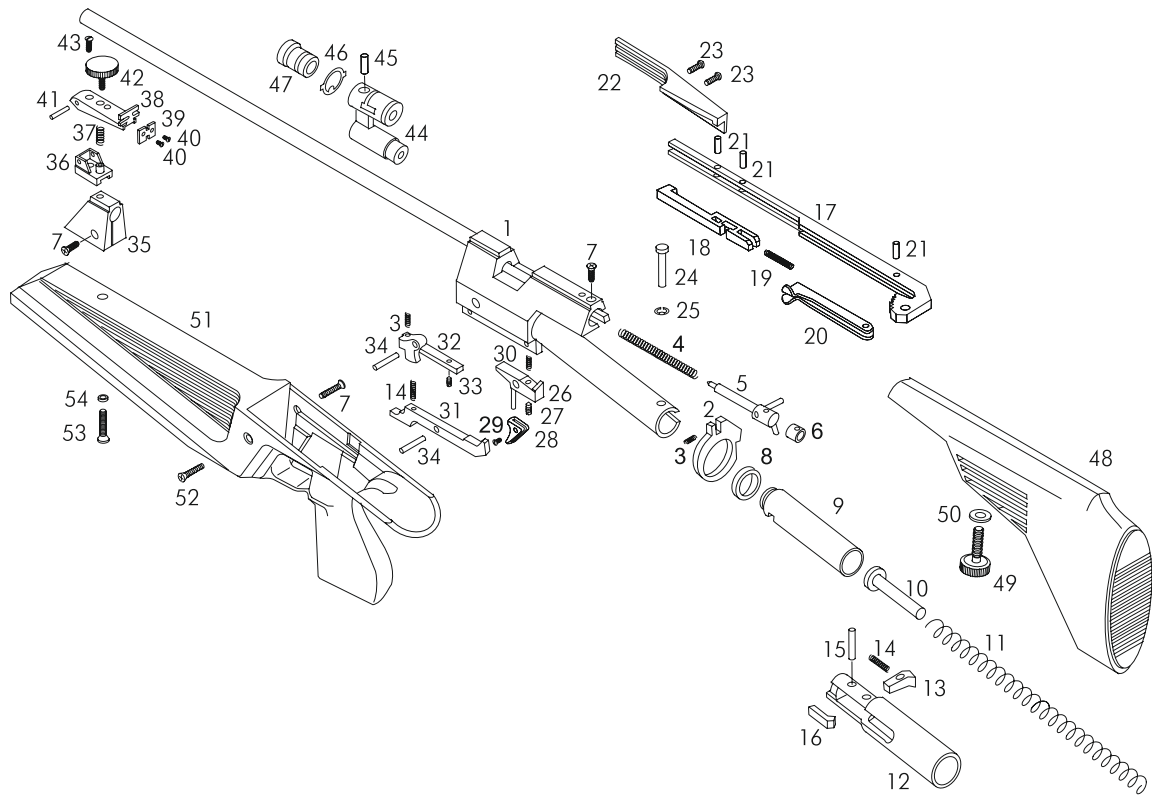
Сборочные единицы и детали винтовки ИЖ-60 – вариант 1
